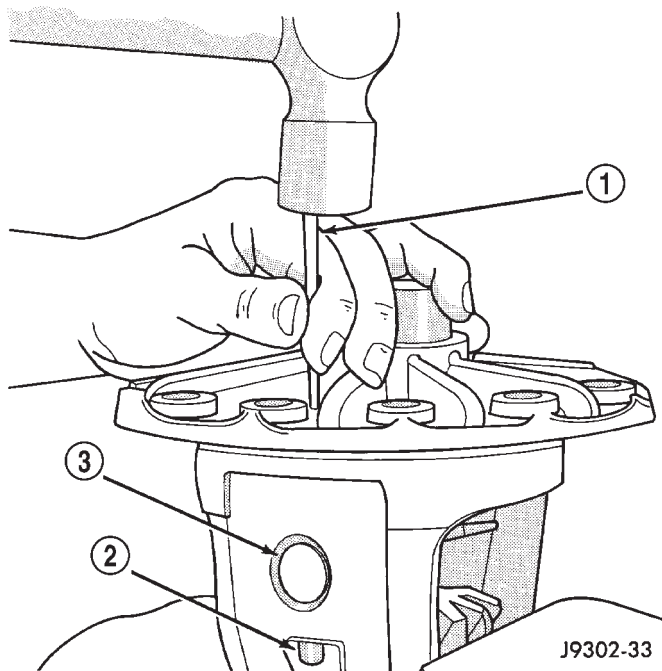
PASADOR DE RODILLO DEL EJE ENGRANADO
